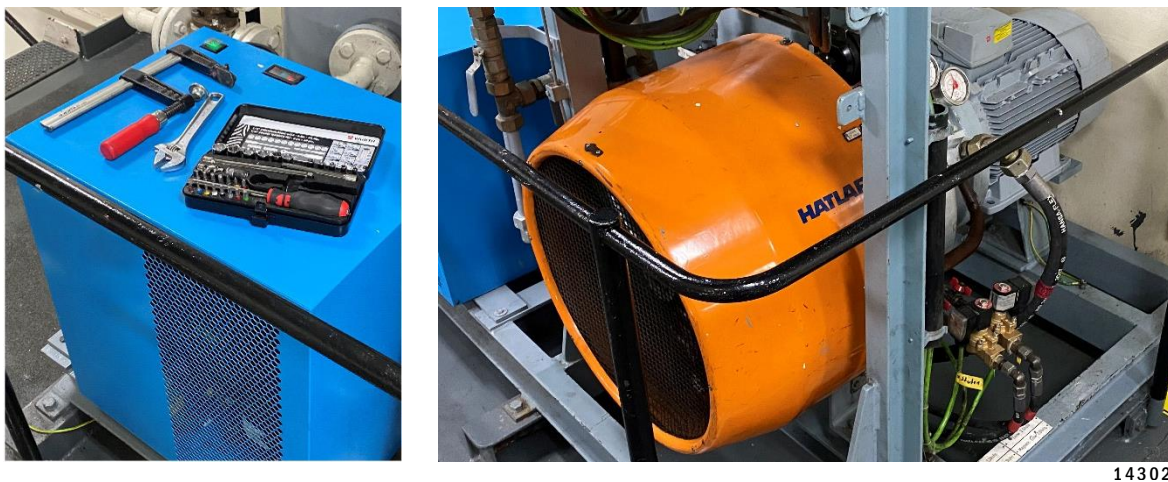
Beispielhafte Einblicke in die Instandhaltung eines Kompressors
